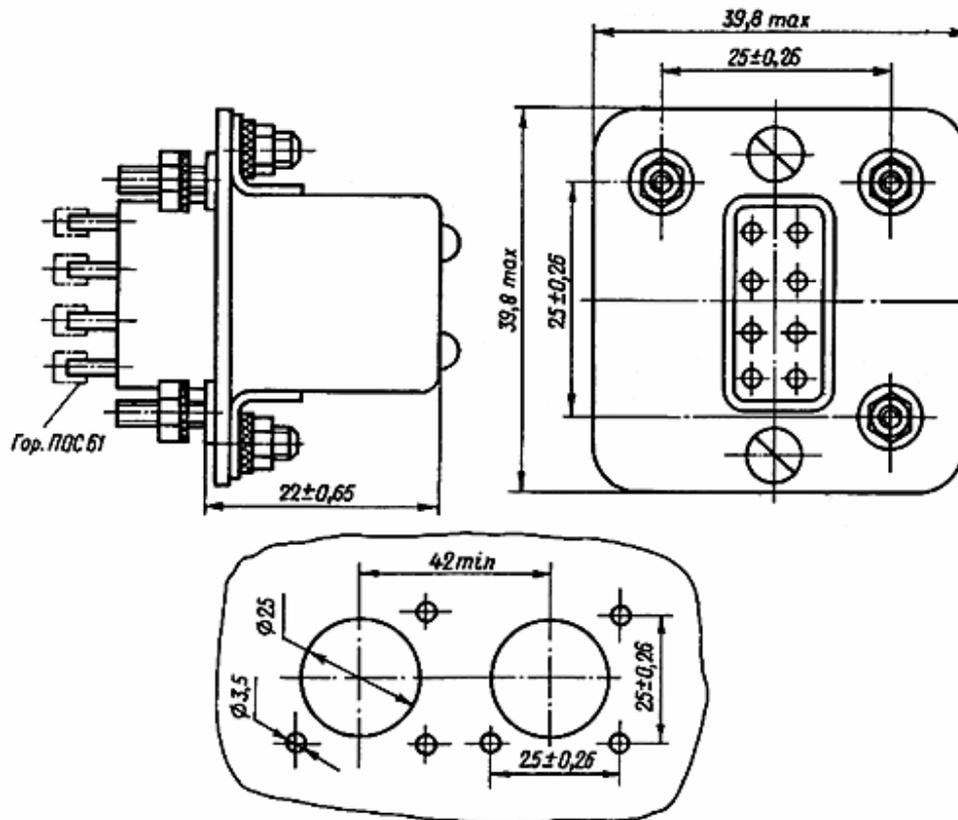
Конструктивные данные реле РЭС59В (с платой для болтового крепления) и разметка для крепления
